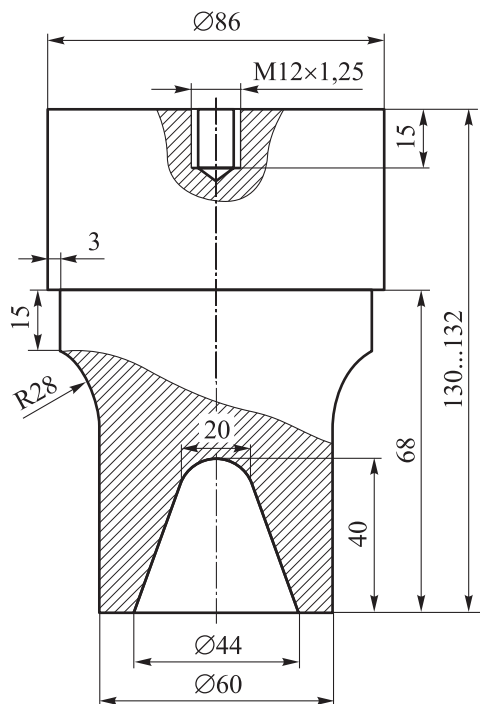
Схема волновода для сварки круглого изделия из полиамида 610
